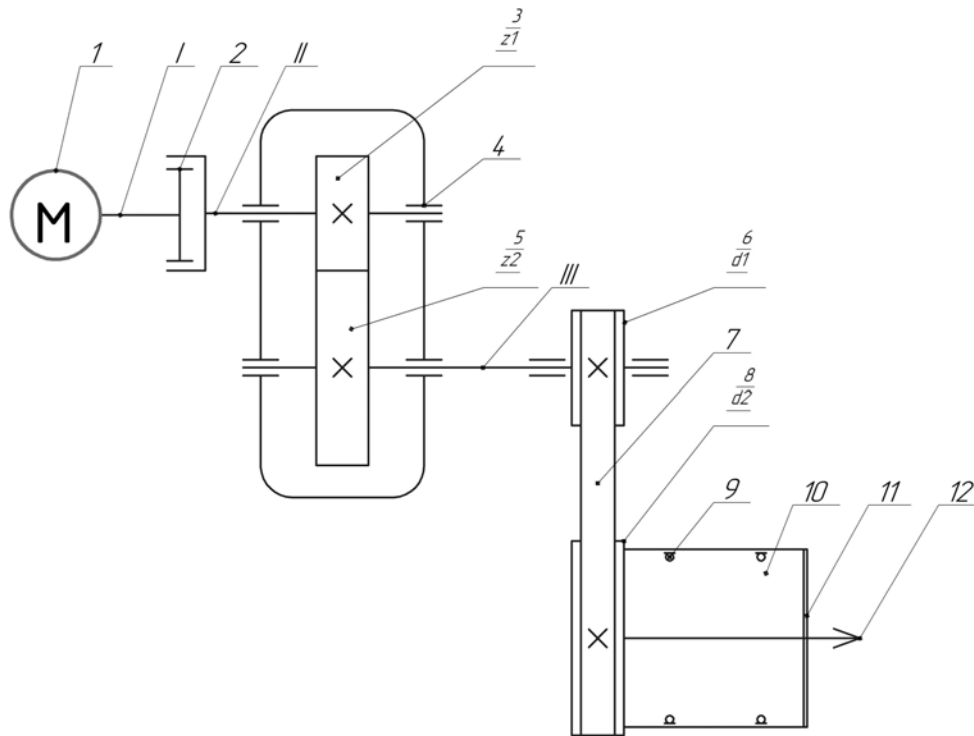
Кинематическая схема механизма резания трубоотрезного станка:
